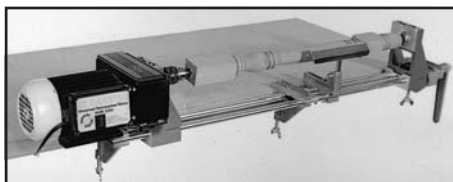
Fig. M: Montage pour des pièces plus grande que 800 mm.
